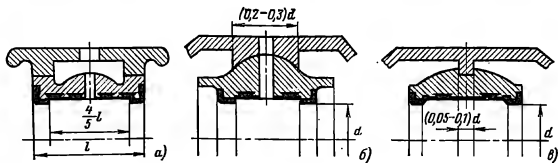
Посадки вкладышей в корпусе подшипника.
